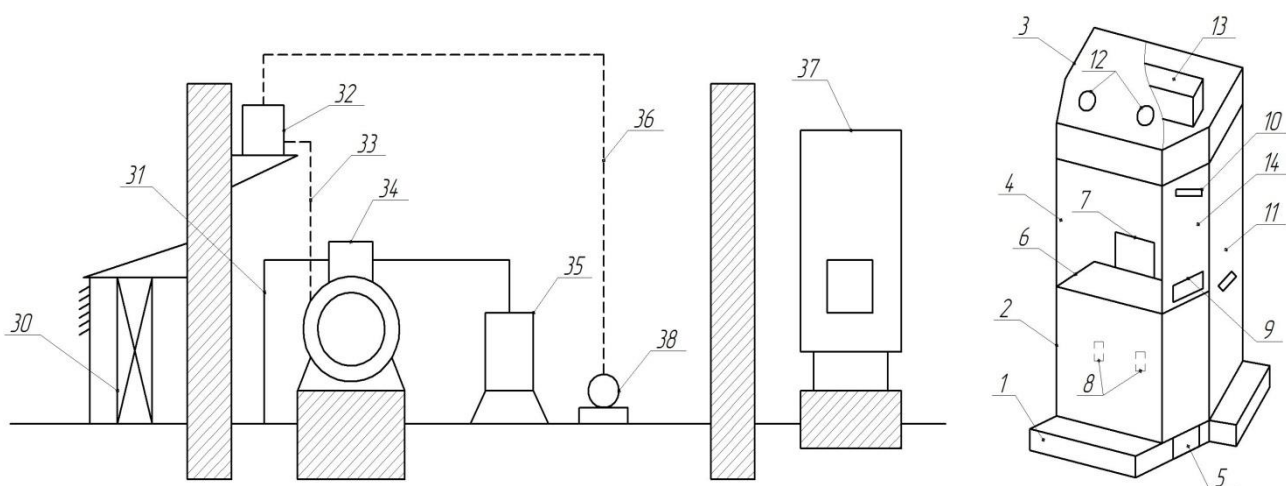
Общий вид стационарной компрессорной установки с акустической кабиной оператора
